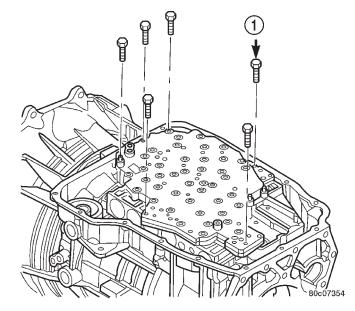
Desmontaje del conjunto de cuerpo de válvulas
